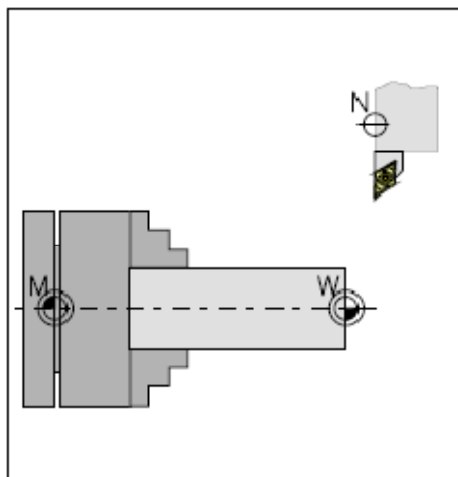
Базовые точки в рабочей зоне токарного станка:
